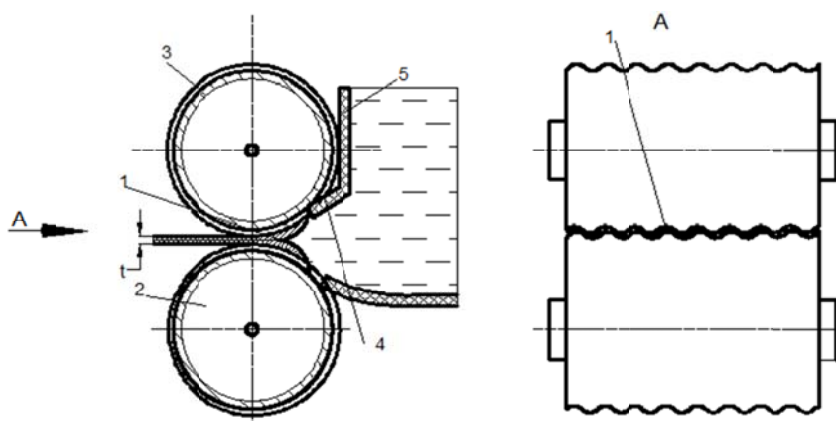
Двухвалковые ПНУРС с горизонтальной подачей металла между профильными валками:
